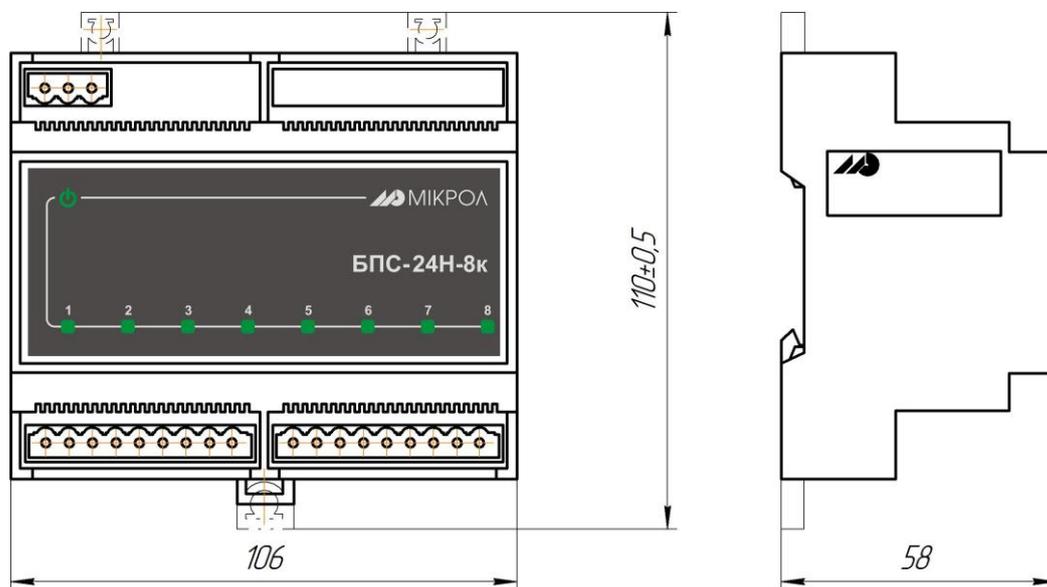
Внешний вид и габаритные размеры БПС-24Н-8к
